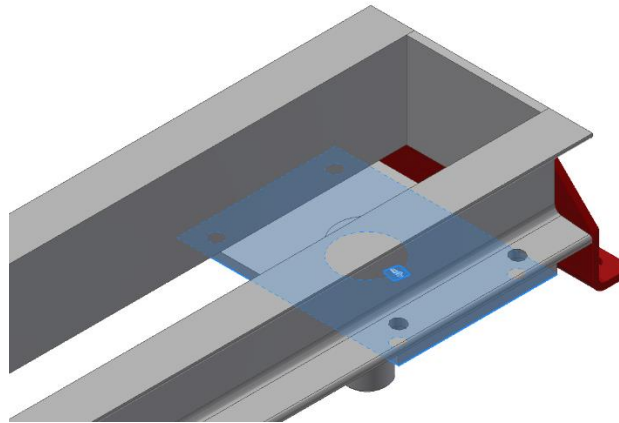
Zona de restrição *Fixed* do braço lateral da estrutura
